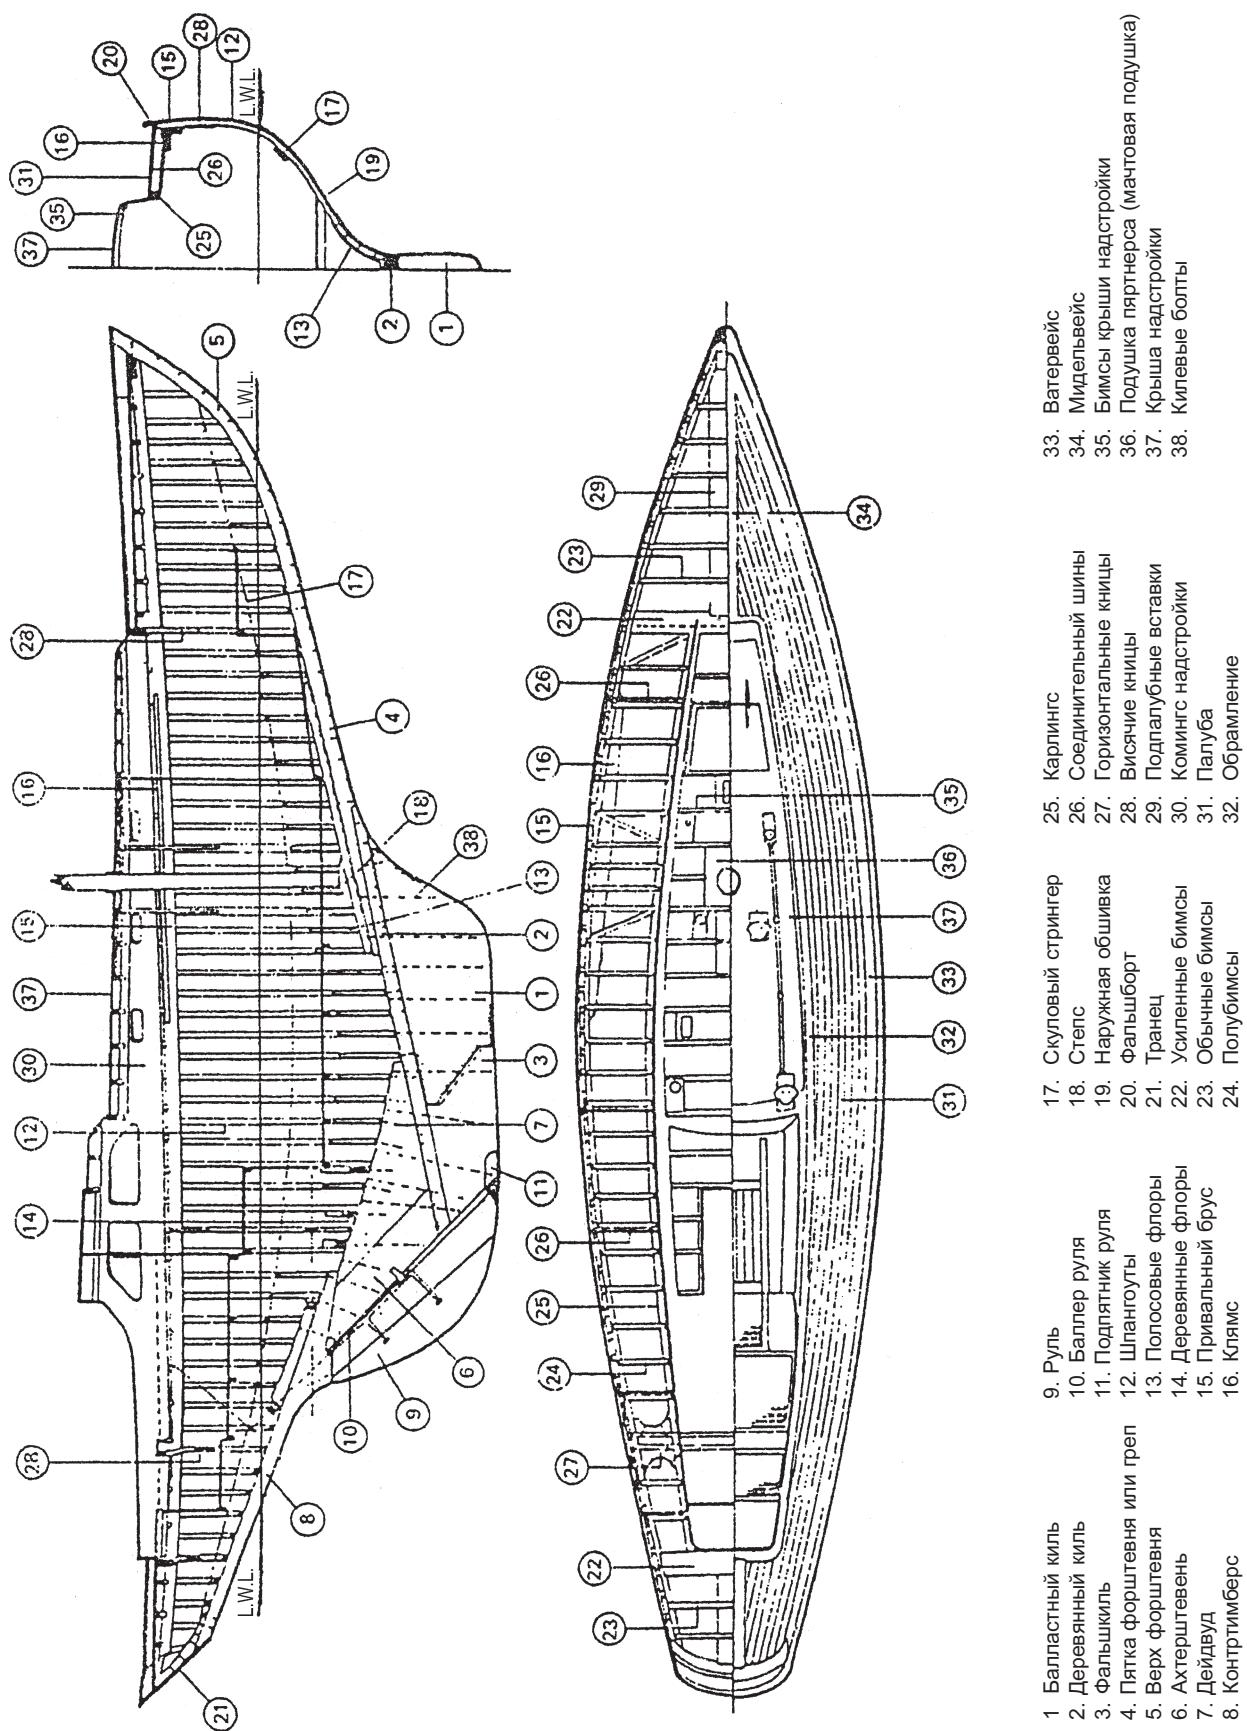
Типовая конструкция корпуса парусного или парусно-моторного судна
